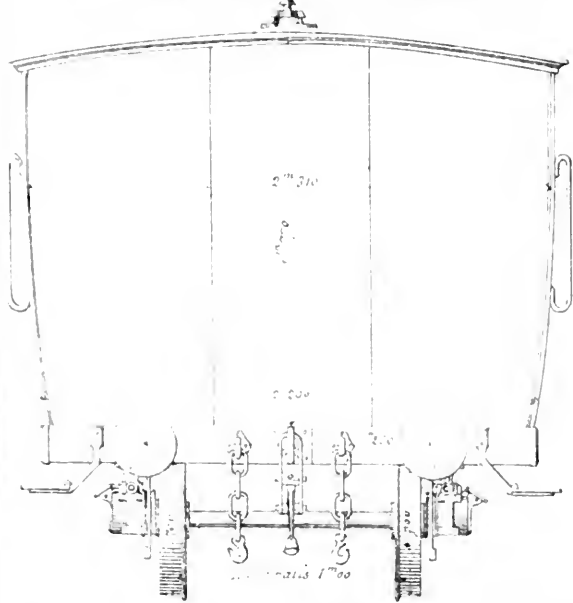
Elevation, Coupe transversale à 0^m03 p^r 1 M^e
